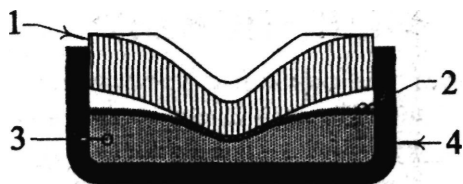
Схема устройства капсюля для нарезного оружия (системы Боксера): 1 - наковаленка; 2 - фольга; 3 - взрывчатая смесь; 4 - колпачок (чашечка)
